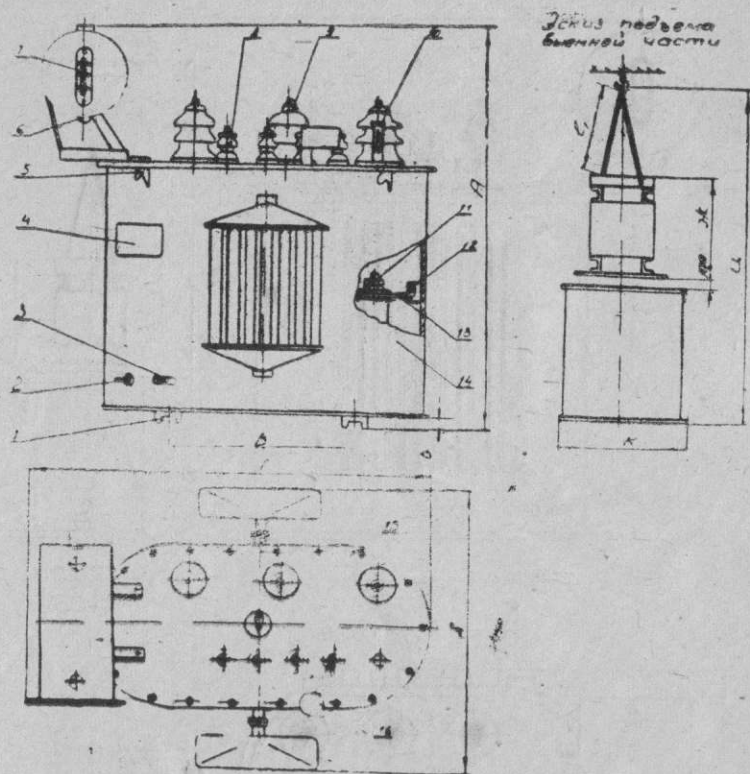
1-балка; 2-заземление; 3-пробка для заливки и отбора пробы масла; 4-щиток мощности; 5-крюк для подъема трансформатора; 6-воздухоосушитель; 7-маслоуказатель; 8-ввод НН; 9-ввод ВН; 10-ртутный термометр; 11-гайка; 12-скоба; 13-пластина; 14-бак; 15-переключатель; 16-предохранитель (устанавливается по требованию заказчика).
